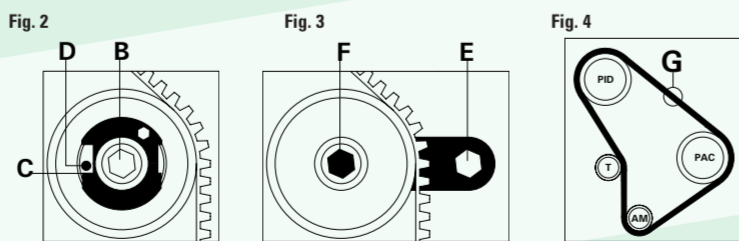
Per motori non turbo: allentare il bullone di bloccaggio B e ruotare in senso orario il tendicinghia fino ad allineare la tacca C con la tacca D, quindi, serrare il bullone di bloccaggio B.
